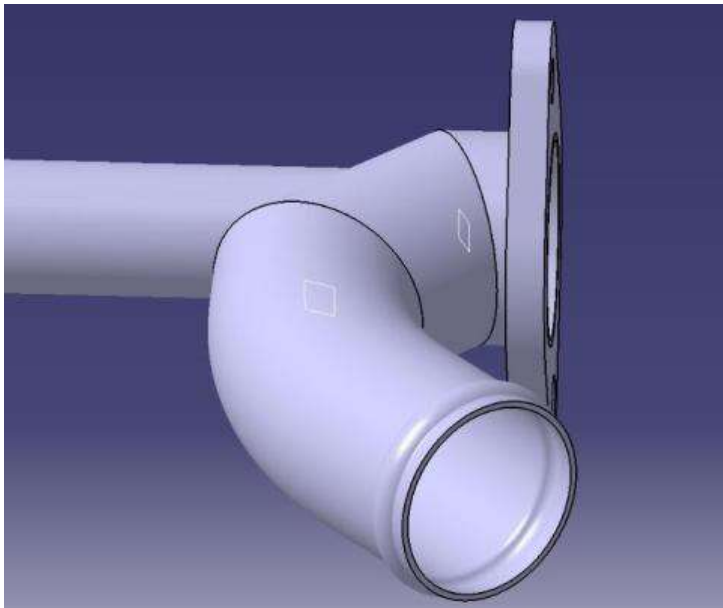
Вид нової частини труби водяного насоса, що підводить.
